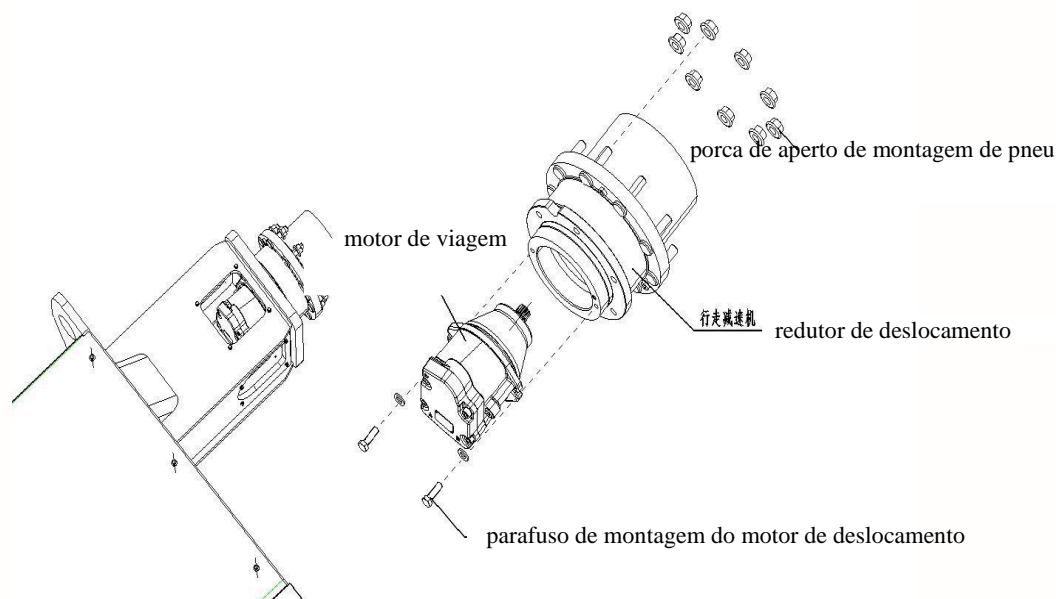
Diagrama de desmontagem do motor de deslocamento
